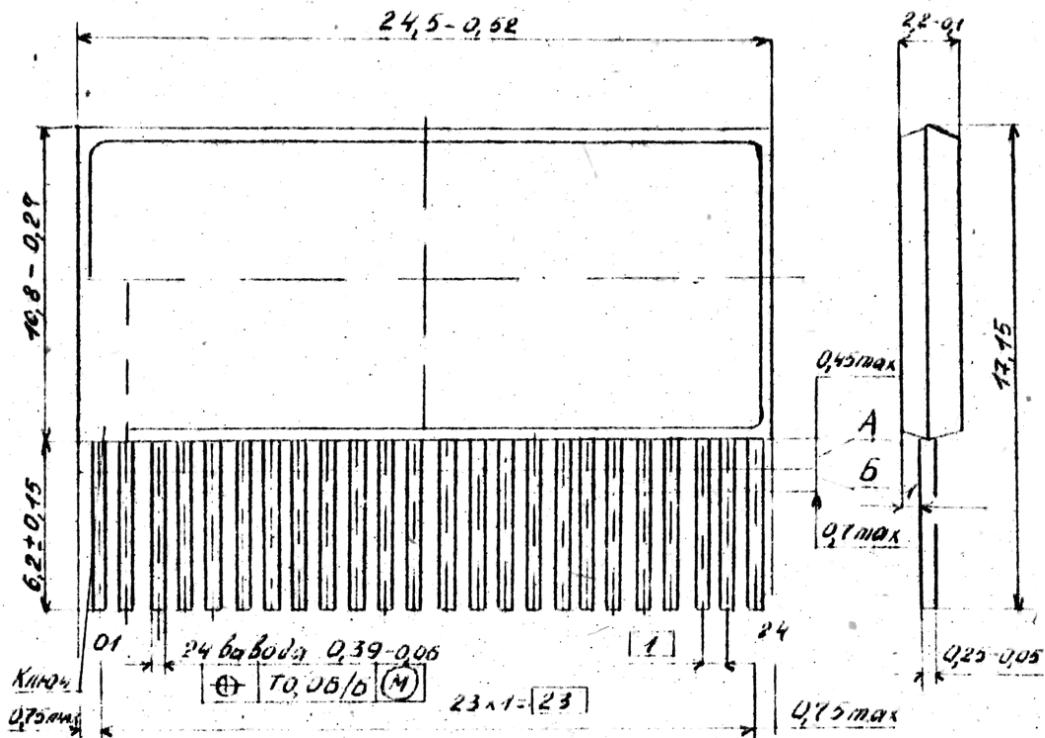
Габаритный чертеж корпуса 4192Ю.24-1
